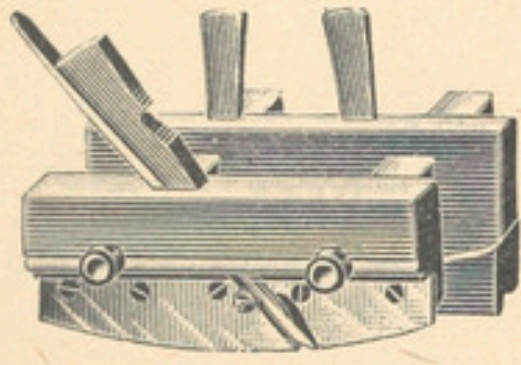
Bouvet à rainure. Fig. 33. — Bouvet rond. Fig. 34. — Outil à entailler.
